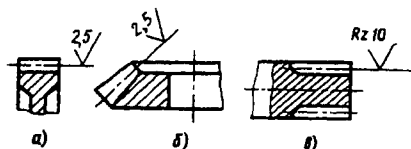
Обозначение шероховатости поверхности зубьев детали без указания их профиля
